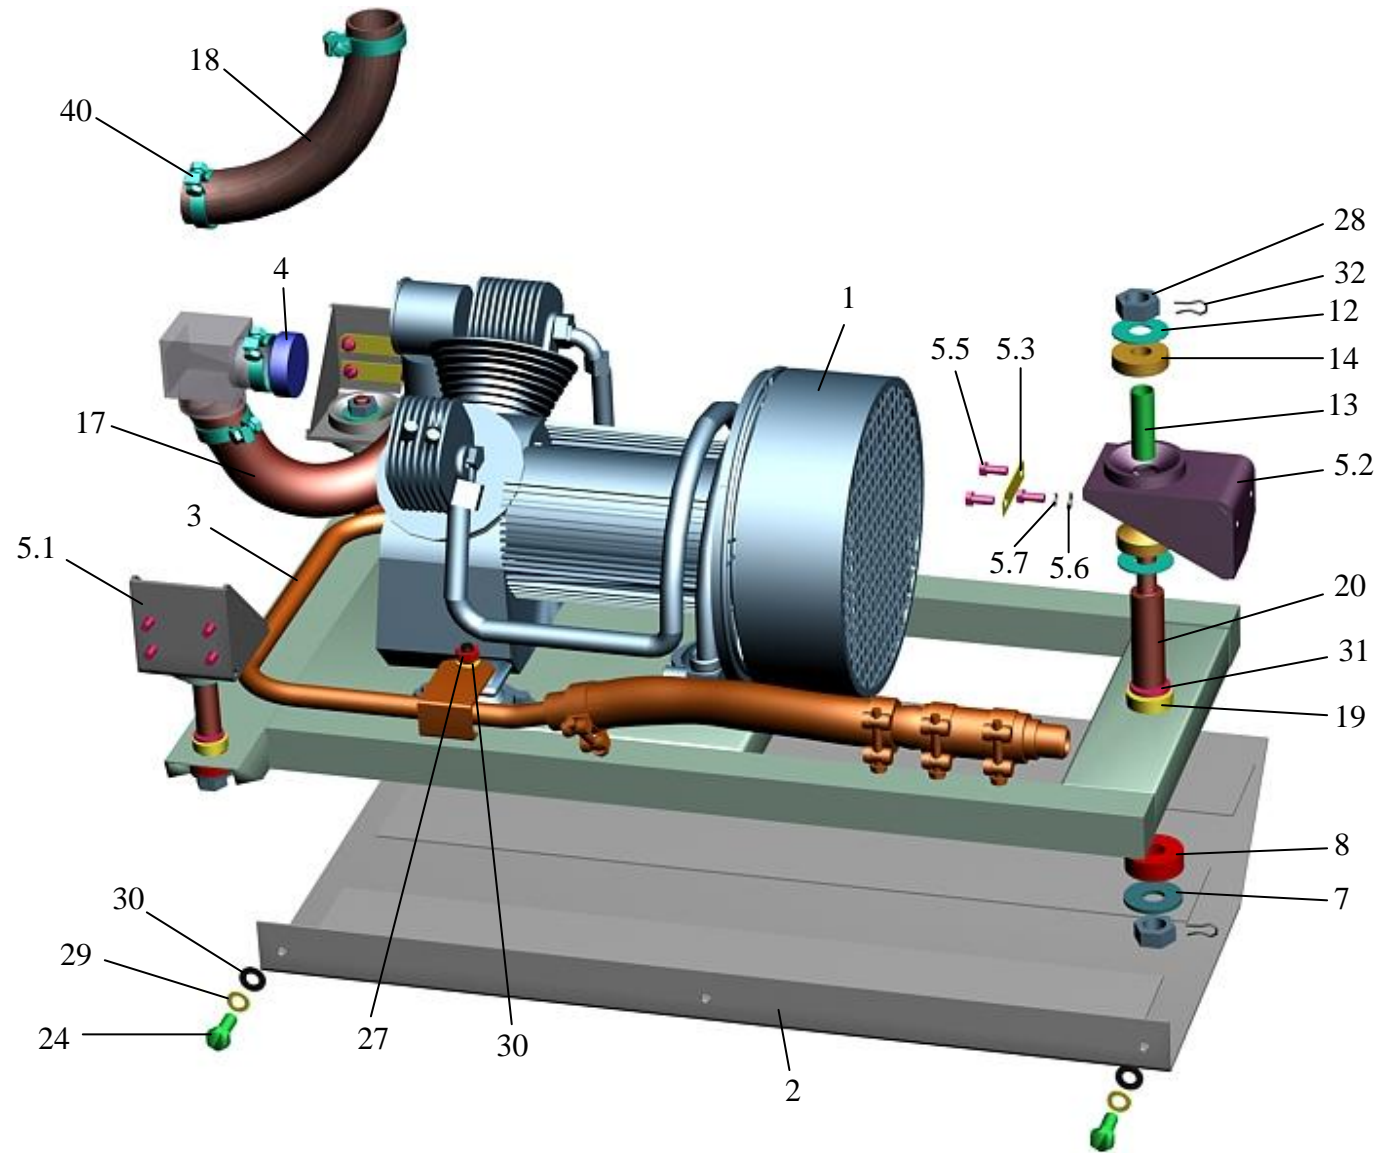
Установка компрессора АКСМ 333-230300.000
